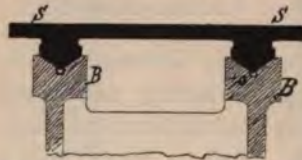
Kraftschlüssige Geradföhrung bei Hobelmaschinen.
